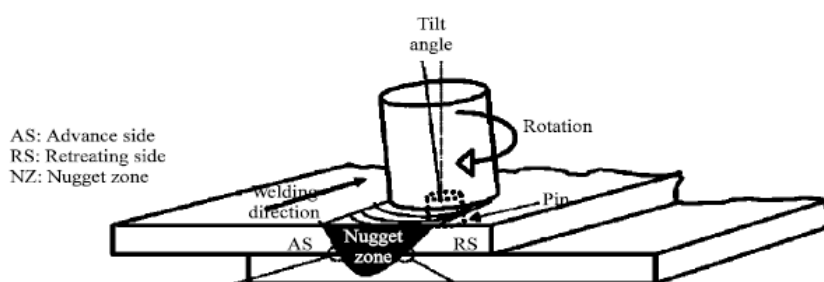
Esquema da soldadura por FSW de uma junta sobreposta onde é apresentado o ângulo aplicado à ferramenta [24].
